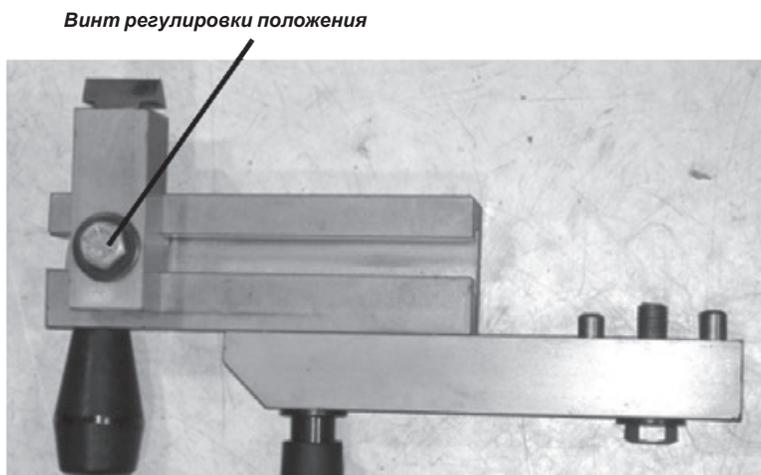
Отверните винт для радиальной регулировки положения выключателя подачи.
